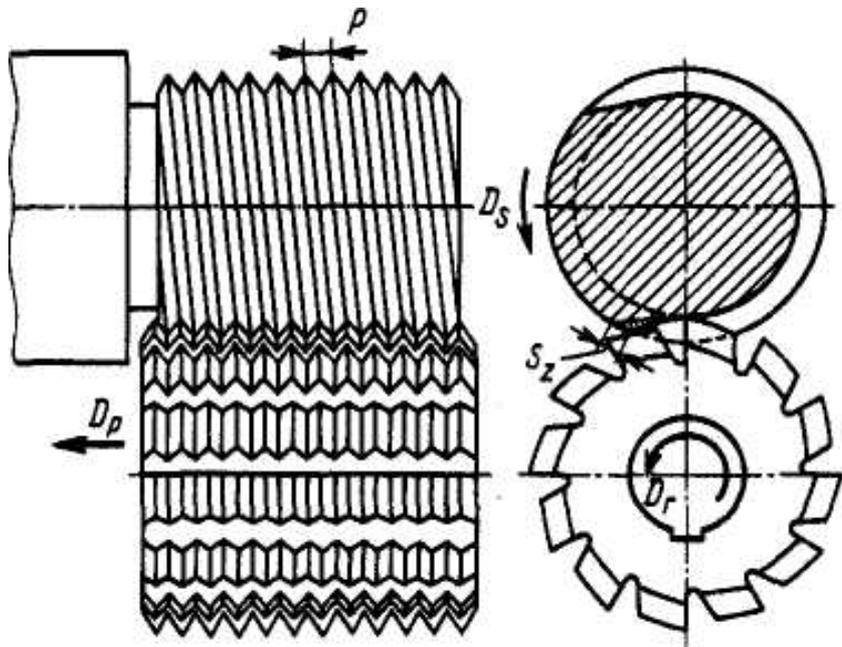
Схема фрезерования резьбы многодисковой фрезой
